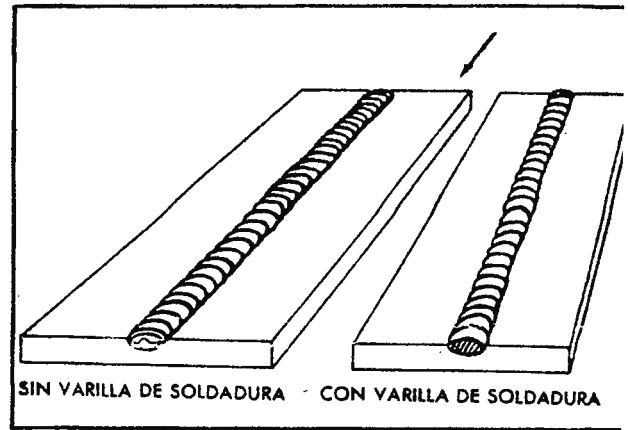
Comparación de soldaduras hechas con y sin material de aporte
